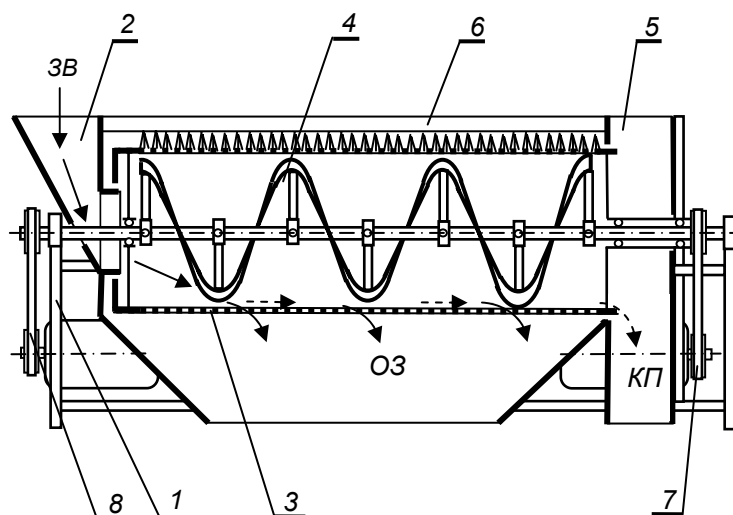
Схема цилиндрического колосового решета с винтовым распределителем:
